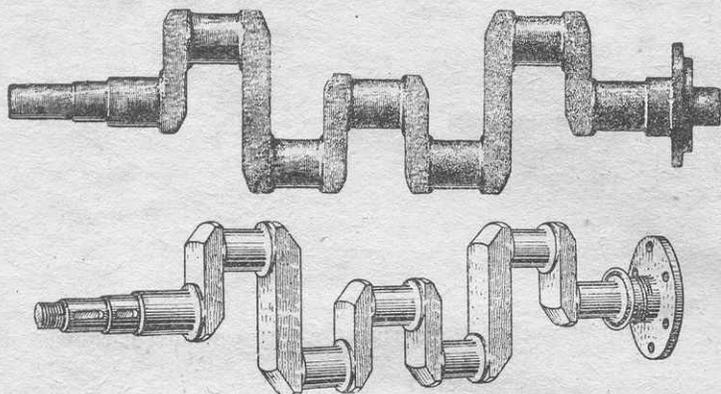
Заготовка (поковка) и обработанный из нее коленчатый вал.
